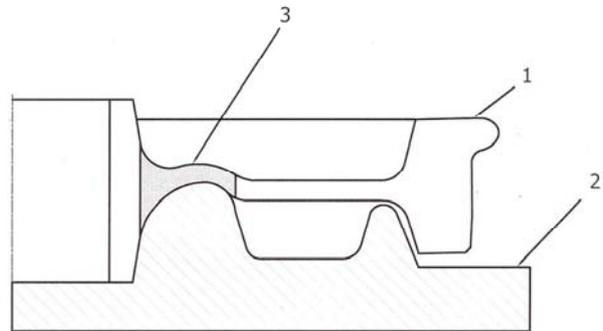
Схема самоцентрировки колеса на прессе 35 МН:
